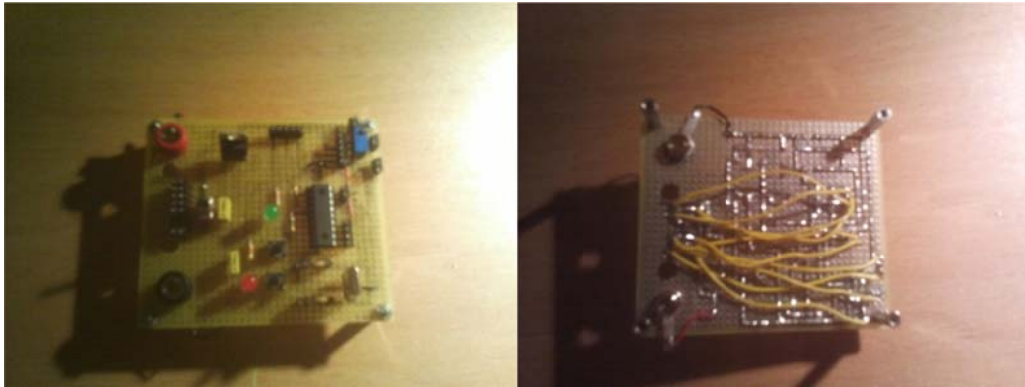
Vista de la cara de componentes y la cara de soldaduras
